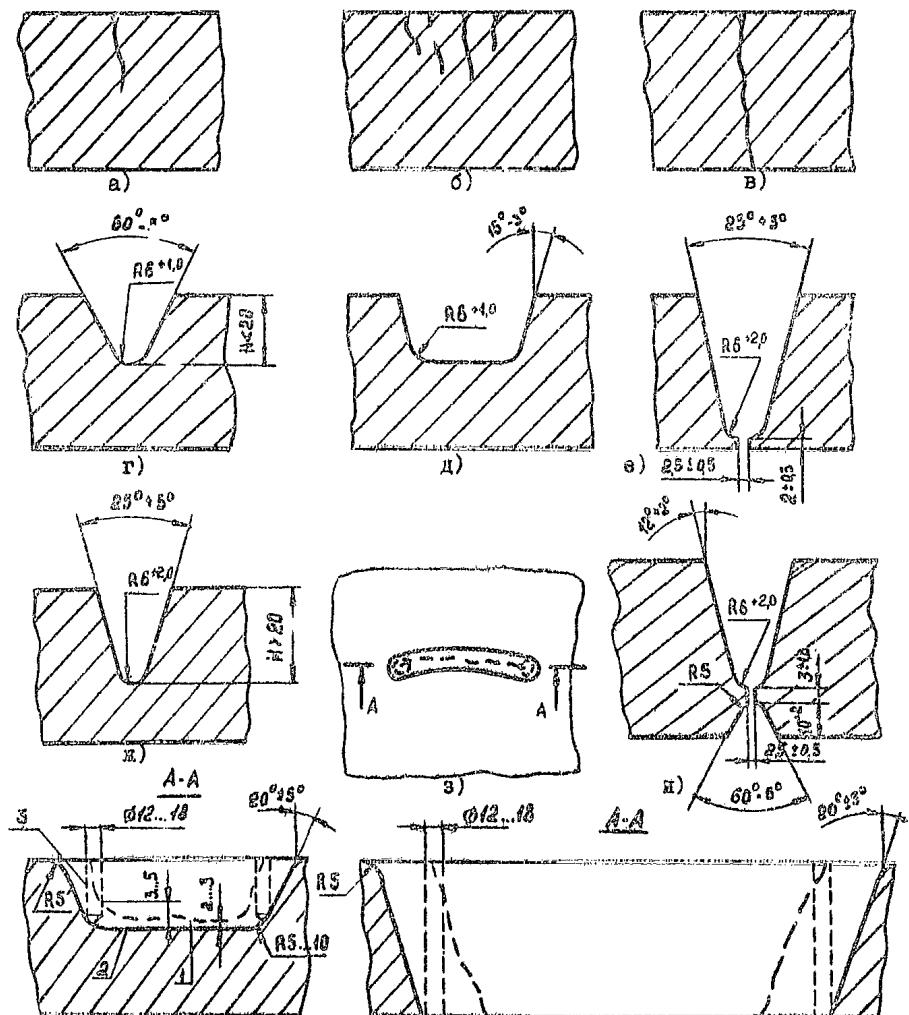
Разделка сквозных и несквозных трещин под дуговую сварку.
